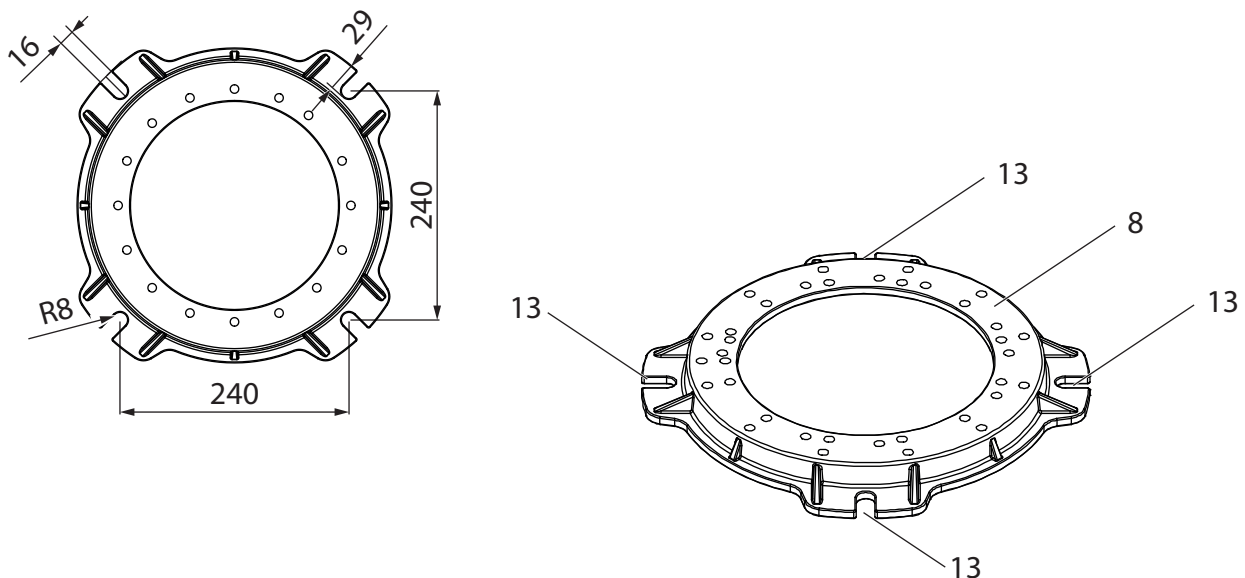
Mechanische Montage – Befestigungsfuß – Beispiel (Maße in mm)
